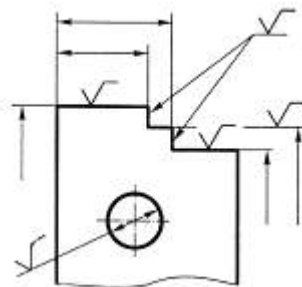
Пример расположения обозначений шероховатости поверхности
